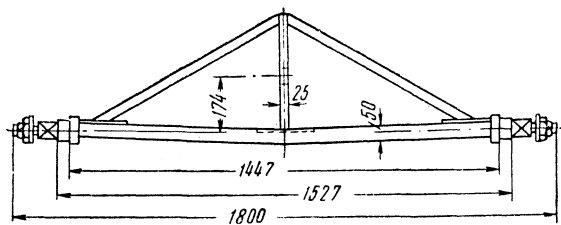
Триангель с глухой посадкой башмака на тележках с вертикальными рычагами
